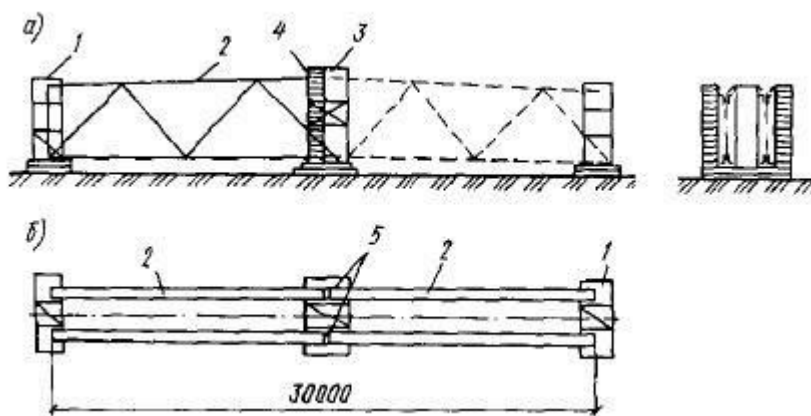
Схема организации рабочего места сборщика монтажных ферм. а) место для установки первой полу фермы, б) вид в плане, 1) крайний кондуктор, 2) полуферма, 3) средний кондуктор, 4) лестница с площадкой для сборки фермы, 5) место сборки стыка фермы
